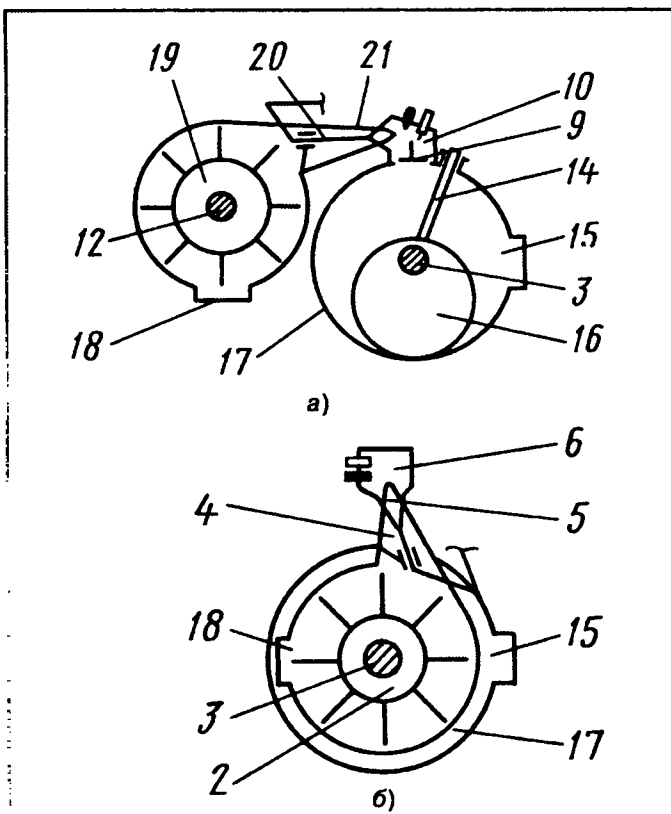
Схемы тяговой турбины (а) и привода вала компрессора (б) (обозначения — те же, что и на рис. 1)
